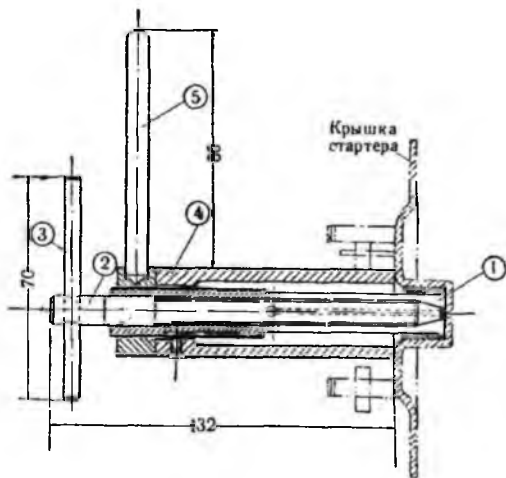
Приспособление для выпрессовки втулки из крышки стартера.
